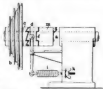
Vorrichtung zum selbsttätigen Ausdrücken der Kupplung an Metallbearbeitungsmaschinen.
